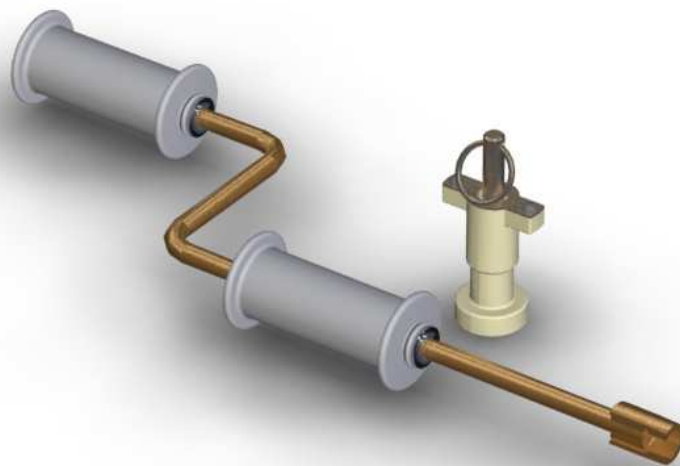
Рукоятка аварийного ручного привода и магнитный ключ КМ-1
